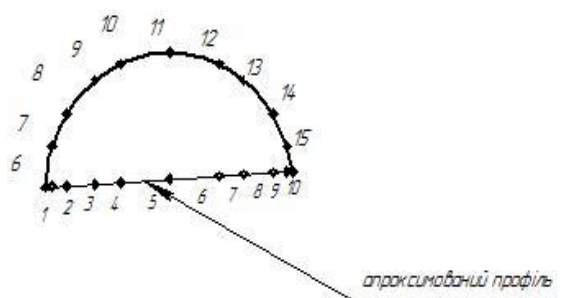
Профілі різця і заготовки сферичної частини профілю
